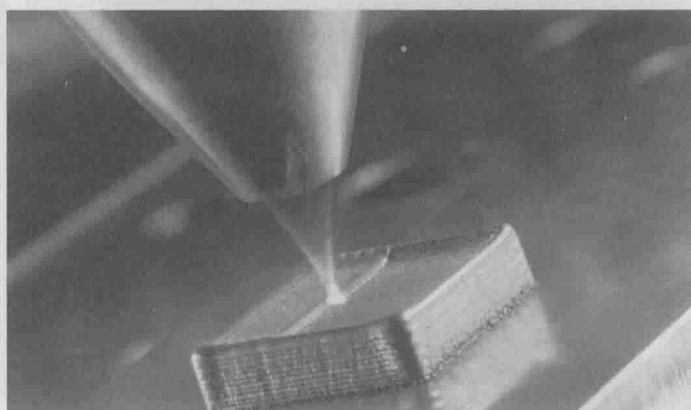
增材制造:在工件上激光沉积焊接
